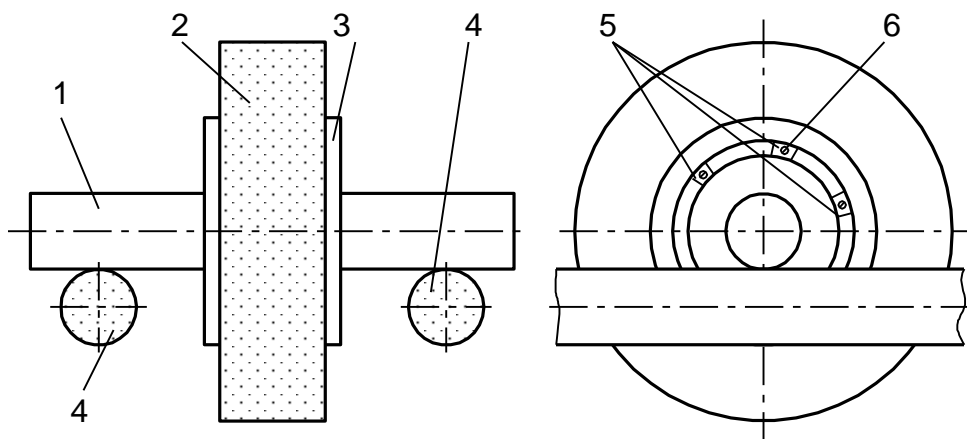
Схема статической балансировки шлифовального круга на станке с цилиндрическими направляющими: 1 - оправка; 2 - шлифовальный круг; 3 - планшайба; 4 - направляющие; 5 - уравнивающие грузы; 6 - крепежные элементы
